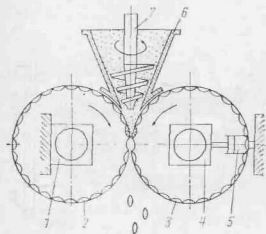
Принципиальная схема двухвалкового брикетировочного пресса
